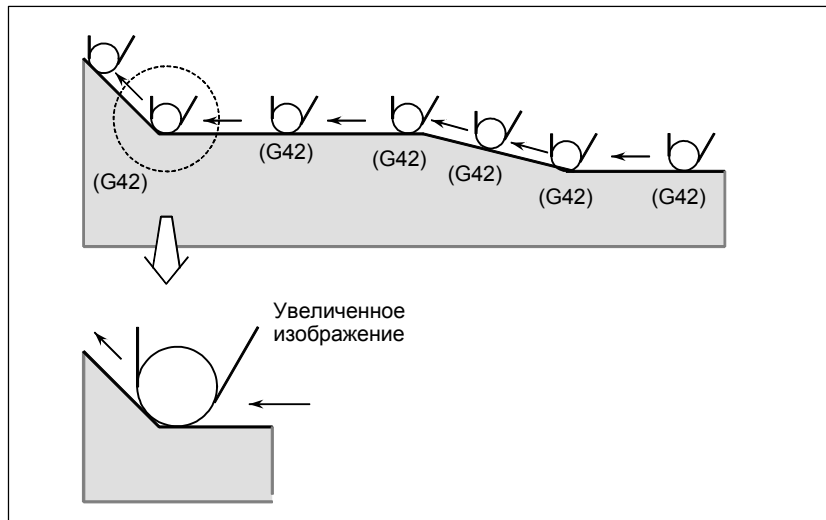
(с) Перемещение инструмента, при котором положение заготовки не меняется
